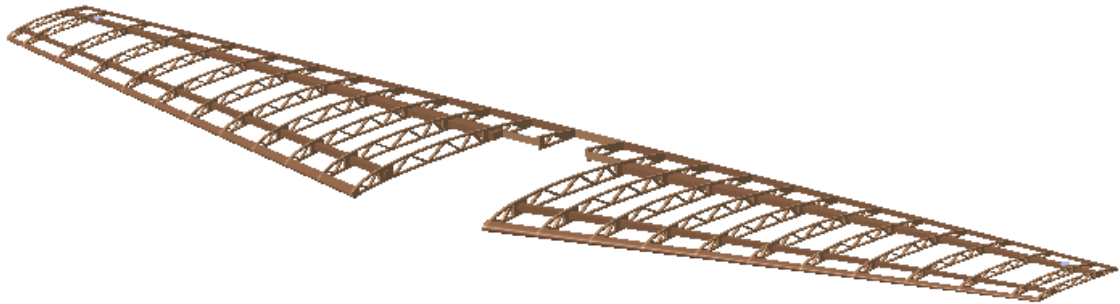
Estructura estabilizador horizontal inferior pintado
